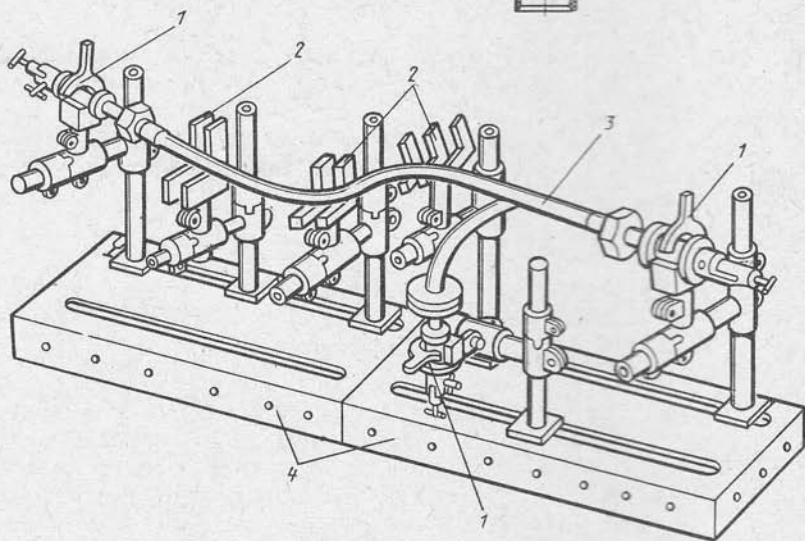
Общий вид универсального сборно-разборного приспособления:
